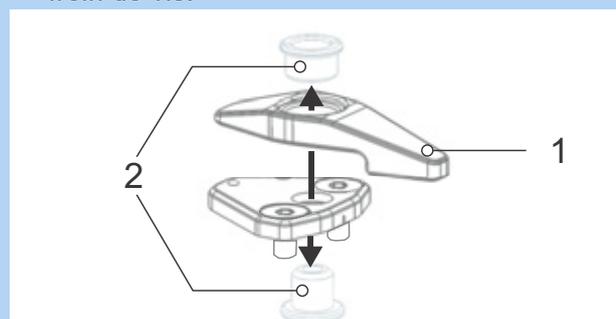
Assembler le levier de blocage avec la plaque de base
